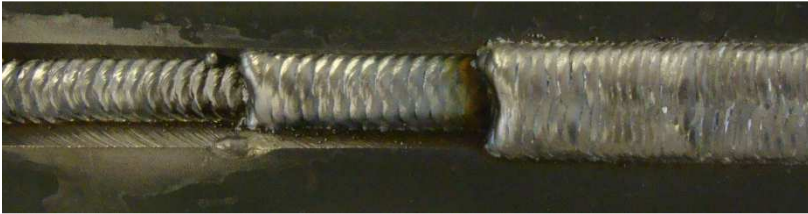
Resultado da soldagem de passes da junta da figura 58
